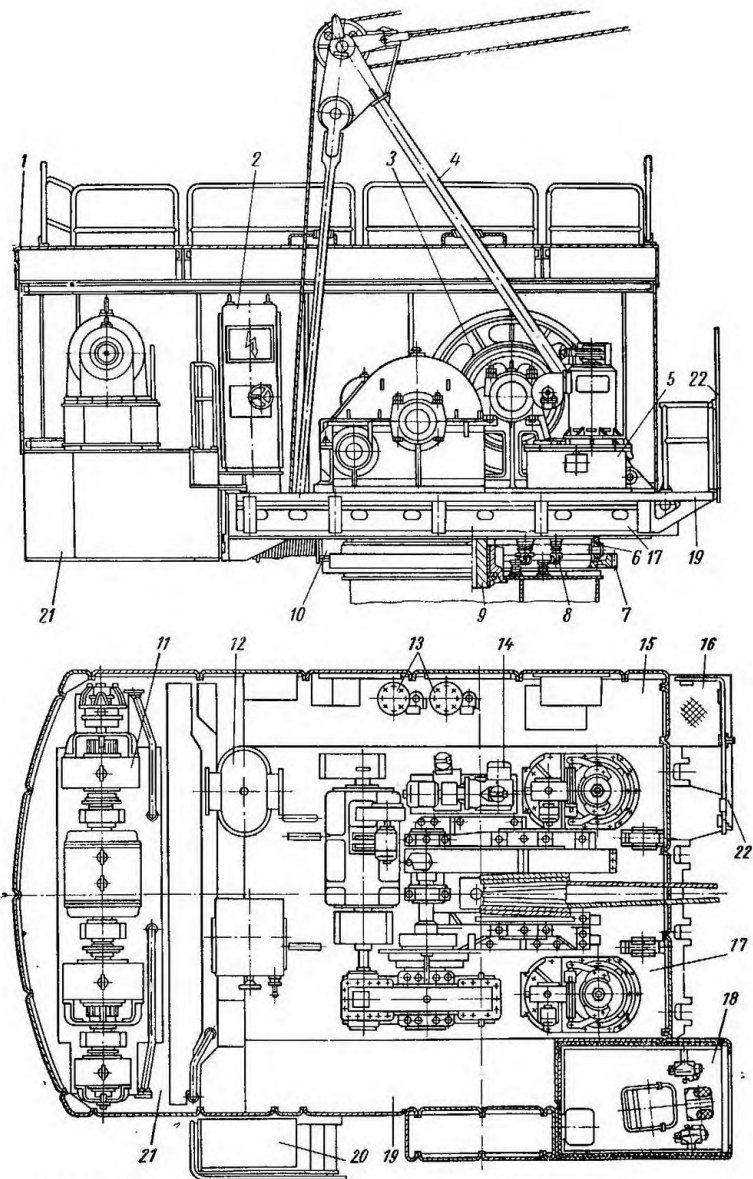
Поворотная платформа экскаватора ЭКГ-4,6А с механизмами
